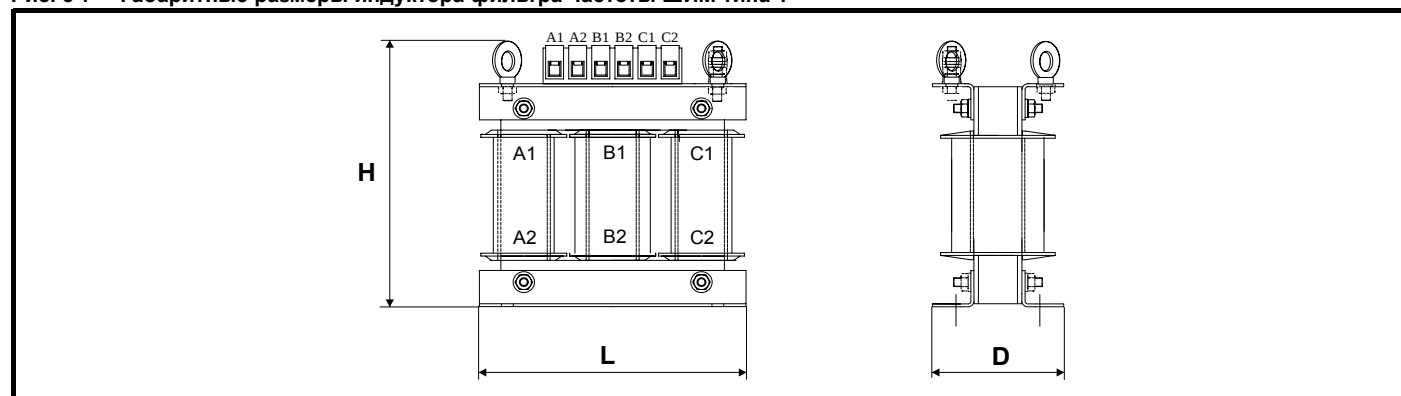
Габаритные размеры индуктора фильтра частоты ШИМ типа 2
